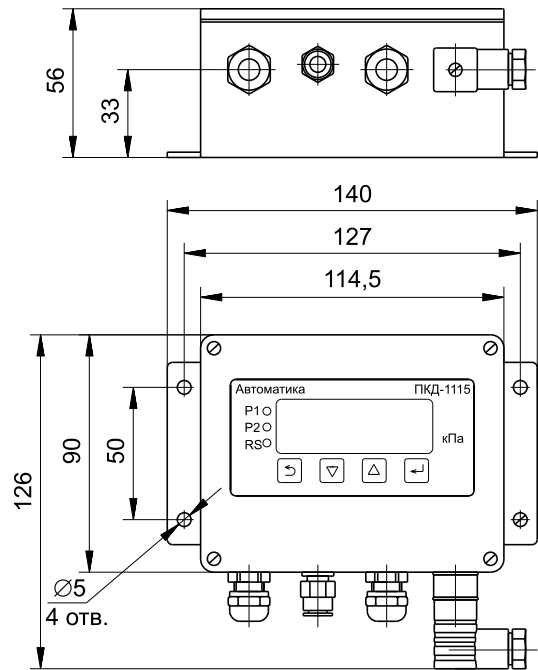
Корпус ПКД-1115 для настенного монтажа
